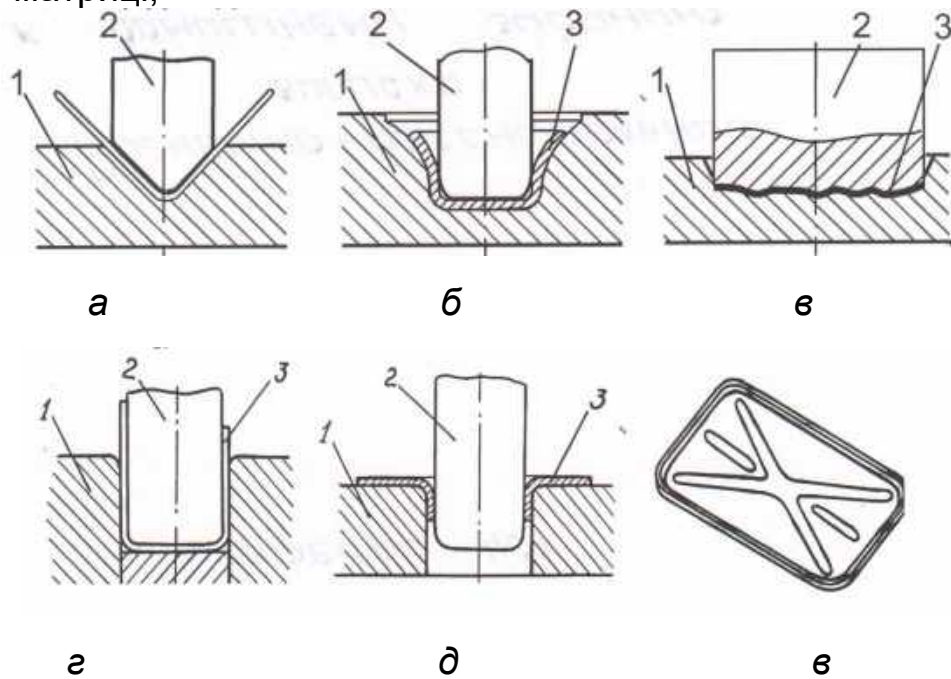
Принципові схеми формотвірних процесів: а – однокутове гнуття; б – двокутове гнуття; в – безпритискна витяжка; г – отбортовка; д – формування; е – відформована деталь (1 – матриця; 2 – пуансон; 3 – заготовка)
